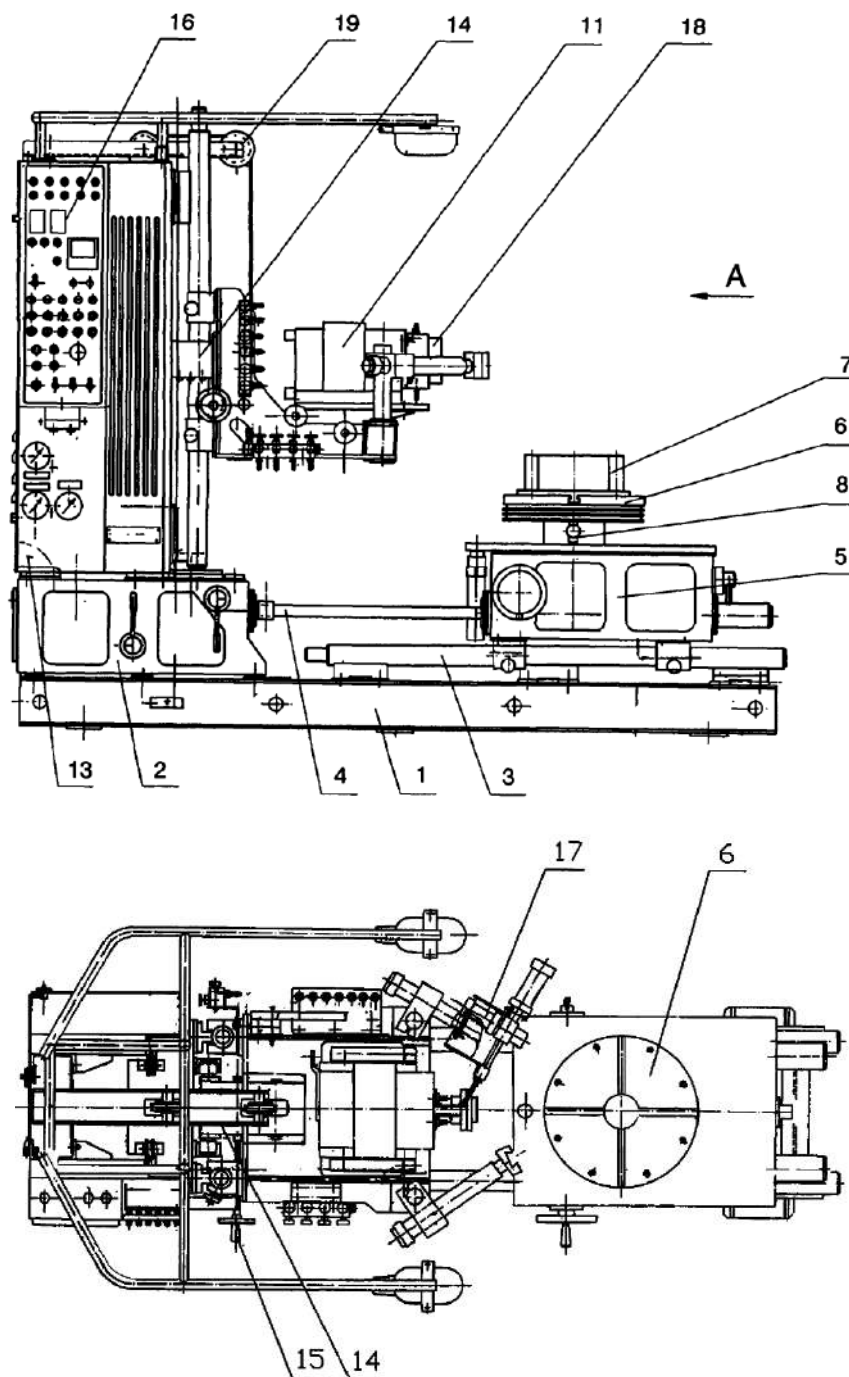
Установка для загартування зубів зубчатих колес
